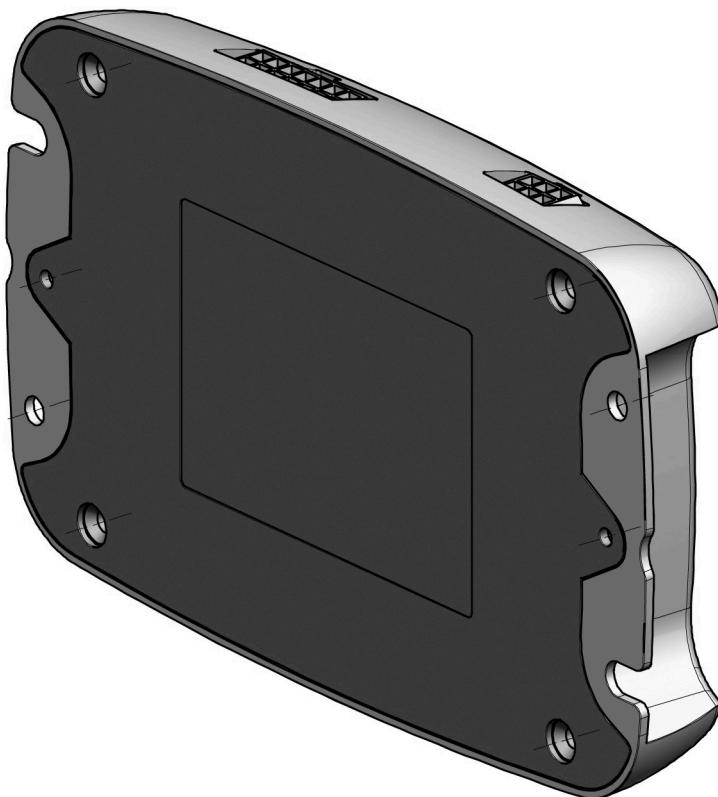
Внешний вид нижней панели корпуса основного блока.
